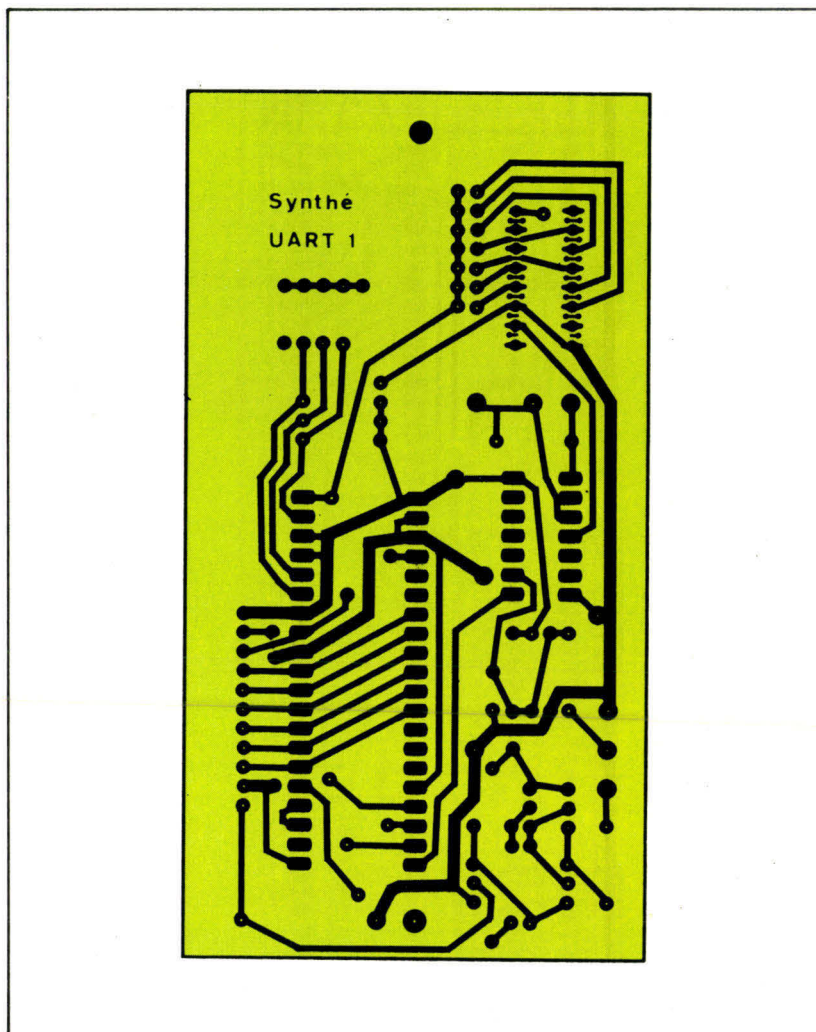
Circuit imprimé vu côté « soudures ».
